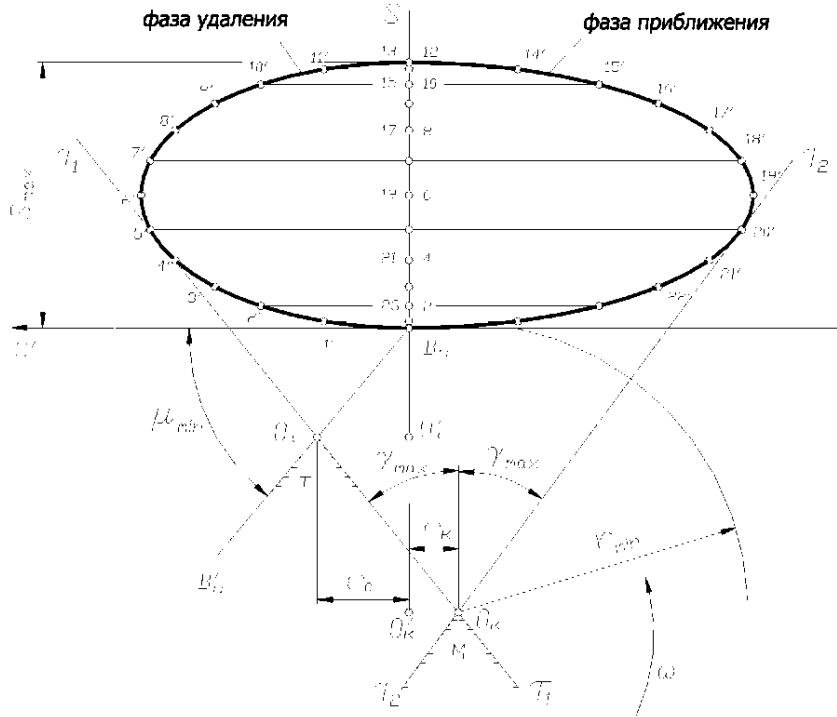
Определение основных размеров кулачковых механизмов с поступательно движущимися роликными толкателями
